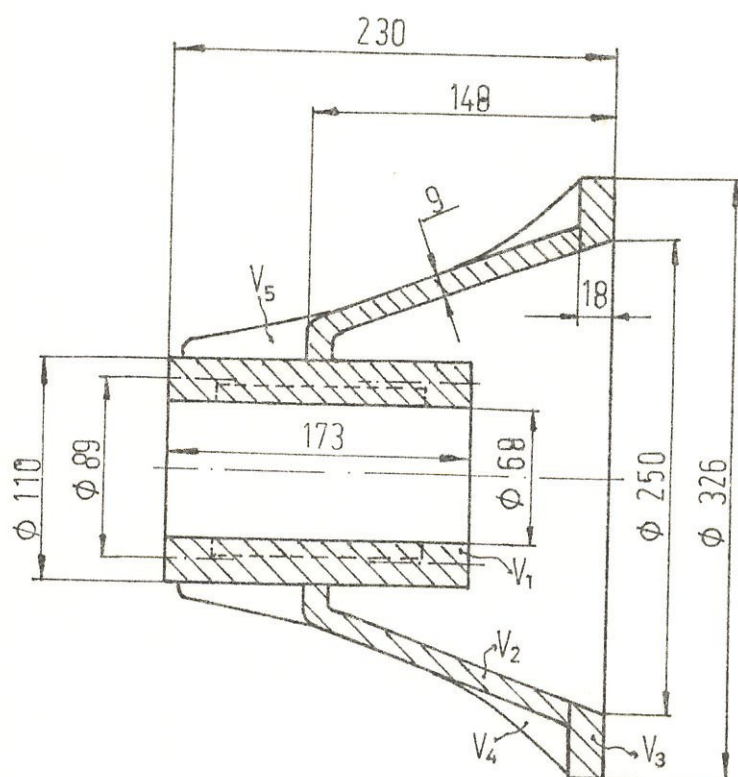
SOPORTE DE RODAMIENTOS.
